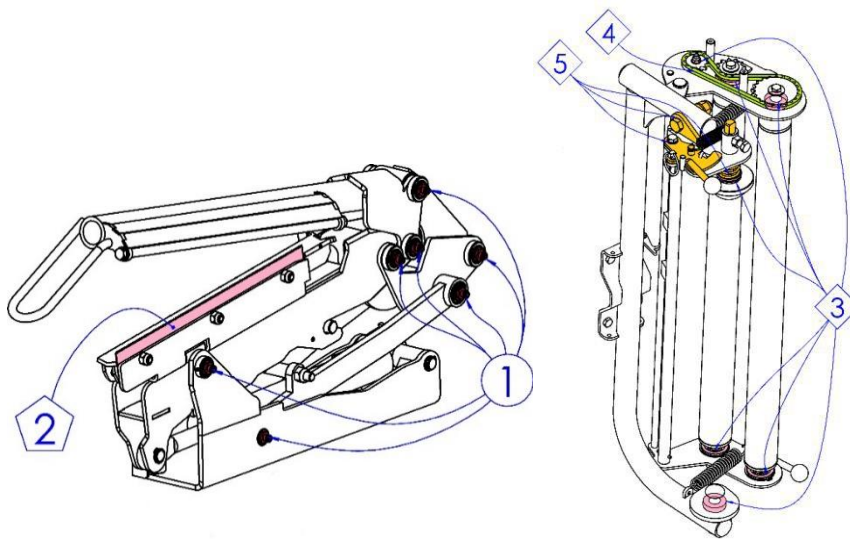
Точки смазки обрезчика пленки и механизма подачи пленки:
